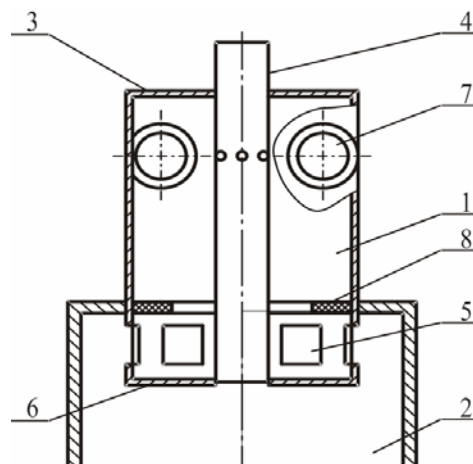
Конструктивная схема центробежно-вихревого деаэратора: 1 – корпус; 2 – центробежный сепаратор; 3 – верхняя торцевая крышка корпуса; 4 – трубопровод отвода пара; 5 – окна для отвода воды из корпуса; 6 – днище корпуса; 7 – подводящие тангенциальные патрубки; 8 – кольцевая перегородка (шайба)
